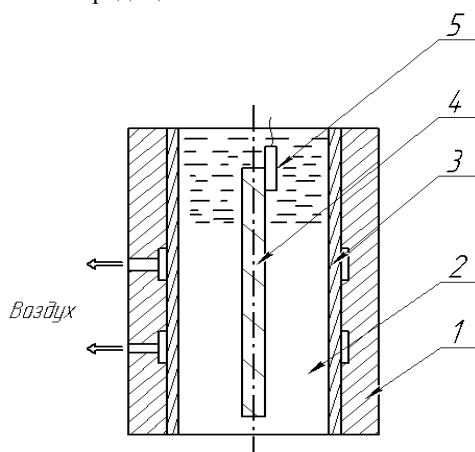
Взрыв заряда БВВ в объеме рабочей передаточной среды над заготовкой, установленной в формообразующей полости инструмента: 1 – матрица, 2 – передающая среда (вода), 3 – заготовка кольцевая, 4 – заряд БВВ, 5 – детонатор
